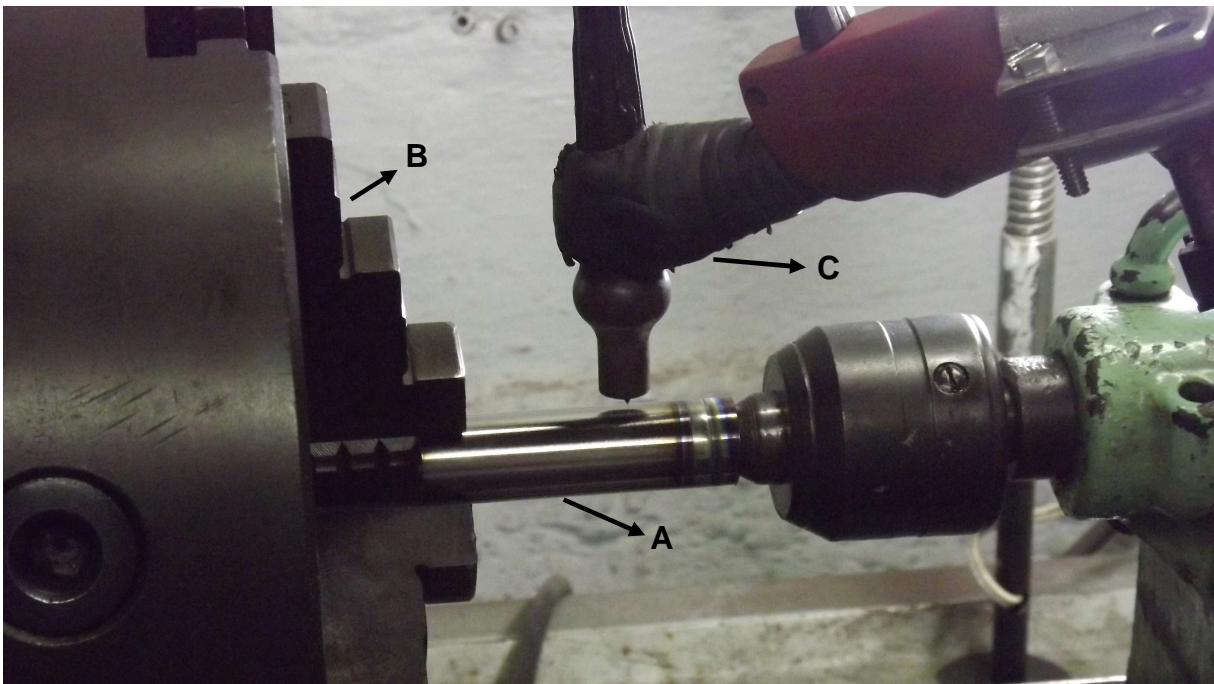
Exemplo do procedimento experimental da soldagem utilizado. Amostra (A) fixada na placa de castanhas (B) de um torno convencional, a tocha de soldagem TIG (C) fixada no porta ferramenta do torno de modo a ficar a 90° com a amostra a ser soldada.
